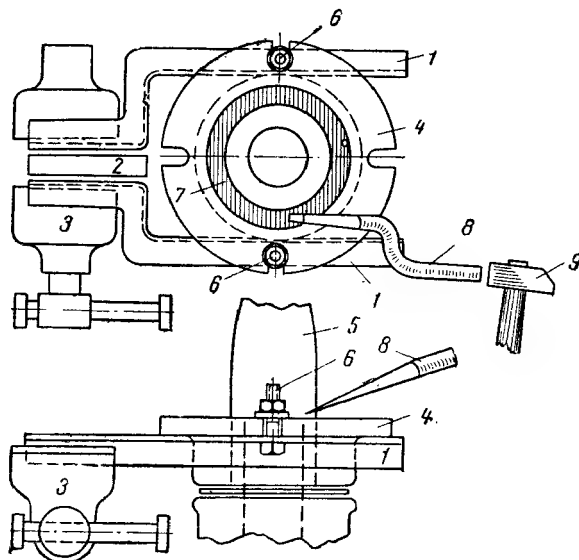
Приспособление для подрубки старой армировочной замазки:
